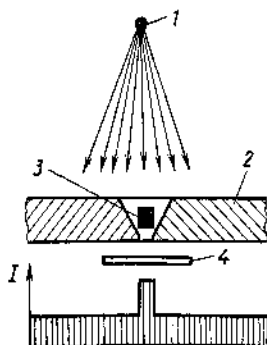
Схема просвечивания сварного соединения:
